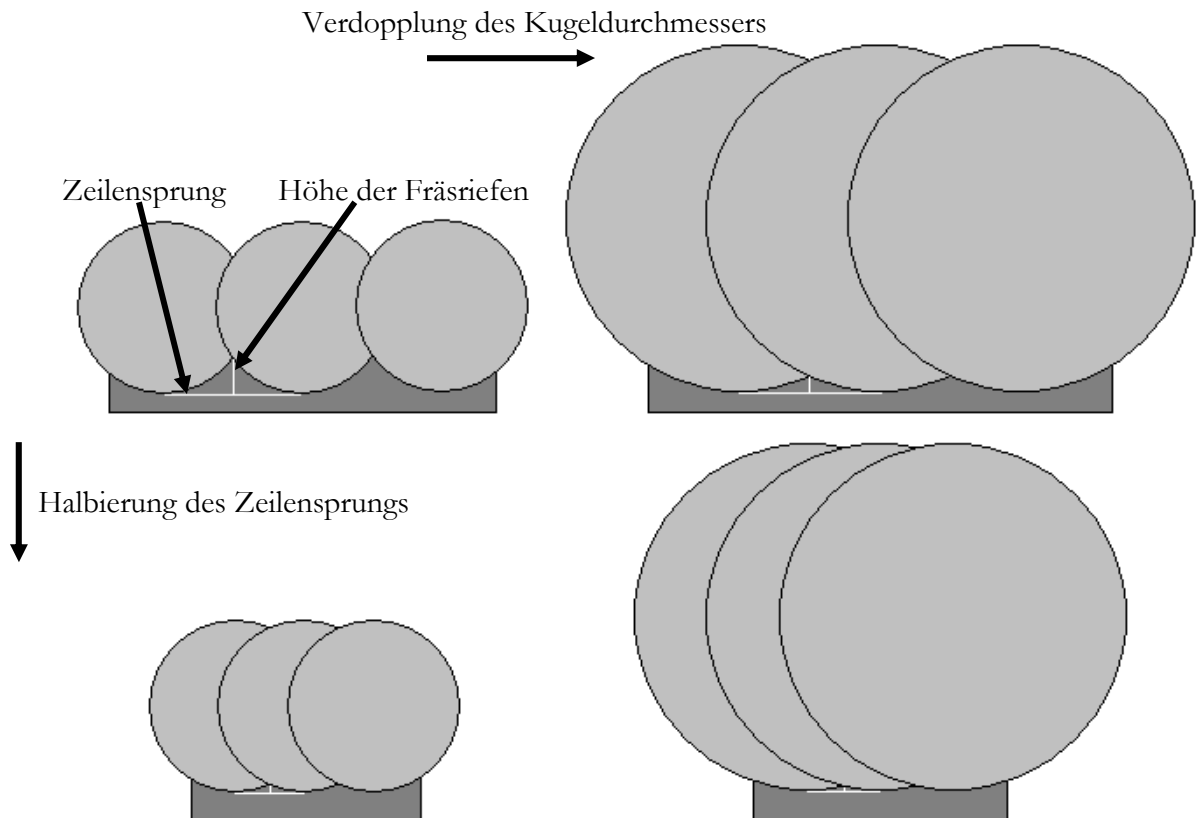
Zusammenhang zwischen der Höhe der Fräsriefen, dem Kugeldurchmesser und dem Zeilensprung
